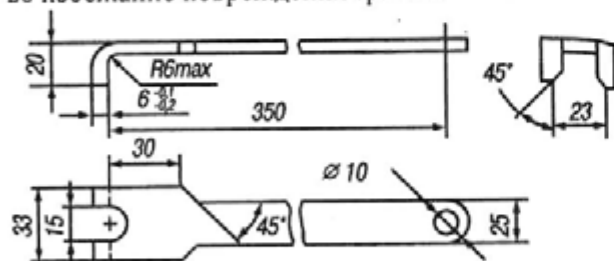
Специальный ключ для отвертывания гайки резервуара
